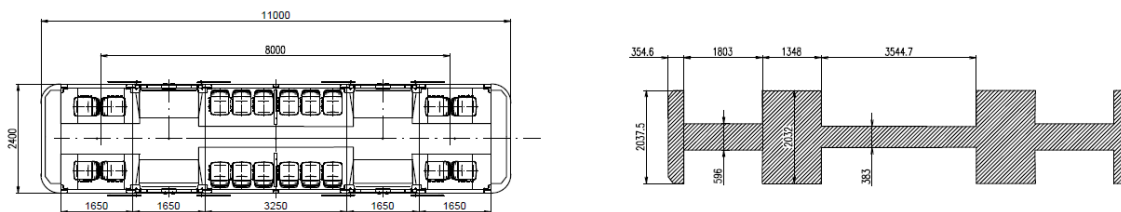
Půdorys uspořádání - varianta 4. [autor DP]
